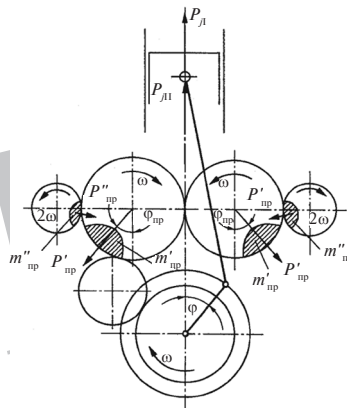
Уравновешивание одноцилиндрового двигателя с использованием противовесов на дополнительных валах
